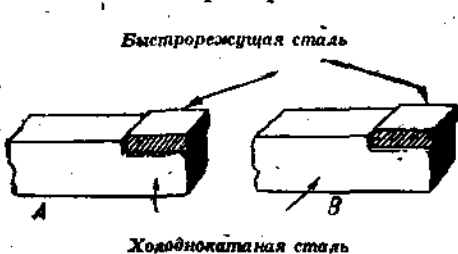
Подготовка к сварке нанесением канавок.
